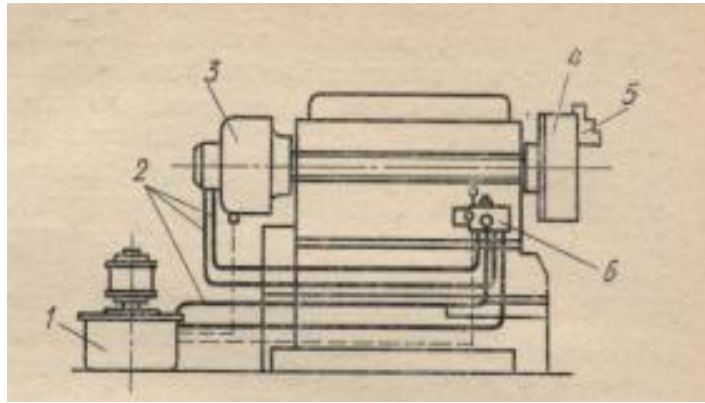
Схема установки гідроприводу на токарному верстаті
